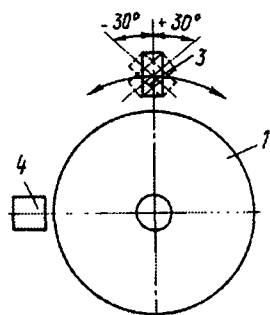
Схема устройства для получения металлической ленты прокаткой расплава
